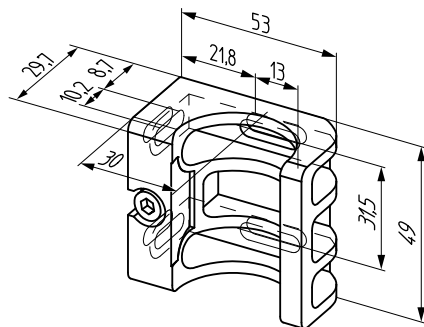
Габаритный чертеж держателя «FlexFix» (2066614)
